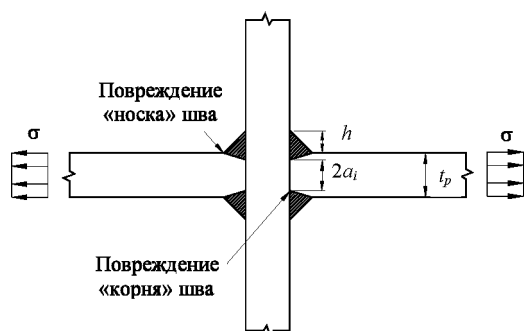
Основные зоны усталостного повреждения сварного соединения
